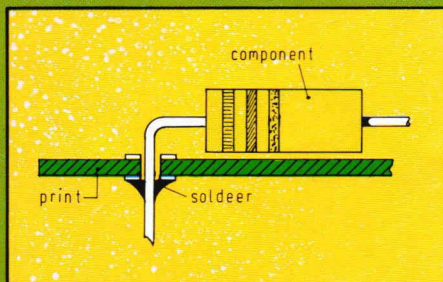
Een goede soldeerverbinding komt tot stand met weinig soldeer.
